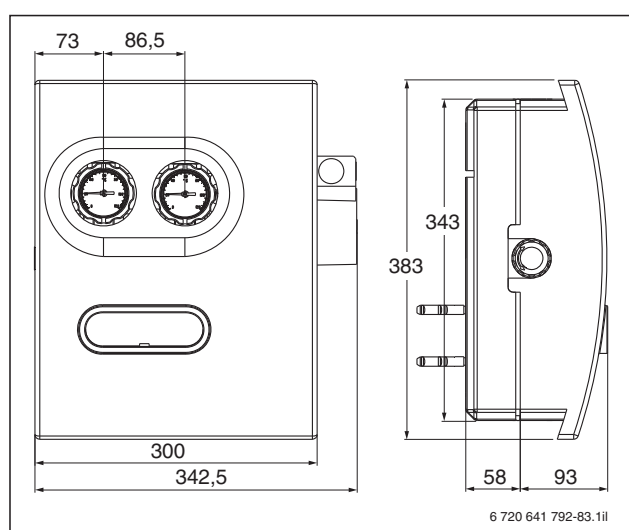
Abmessungen Warmwasser-Mischergruppe mit Zirkulationspumpe (Maße in mm)
